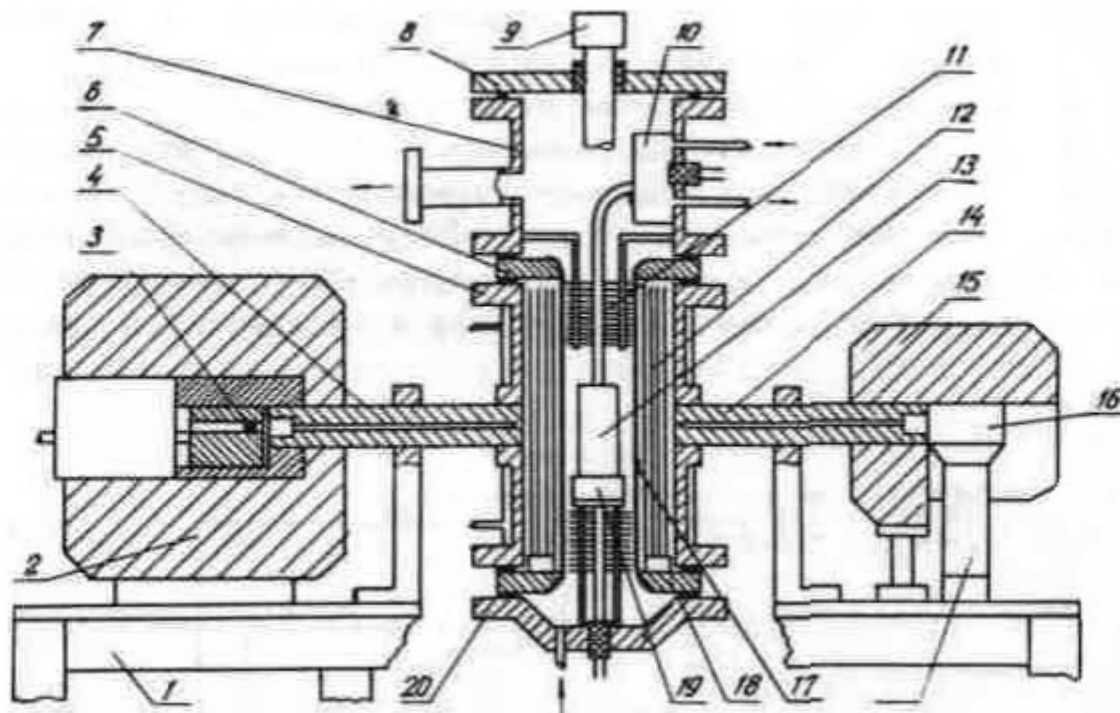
Принципиальная схема гамма-плотномера: 1 - опорный стол; 2, 15 - защитный контейнер; 3 - источник излучения; 4, 14 - коллиматоры; 5 - корпус печи; 6, 18 - токоподвод; 7 - форвакуумная камера; 8, 20 - крышки; 9 - загрузочное устройство; 10 - термостат холодных спаев; 11, 12 - экраны; 13 - измерительная ячейка с образцом; 16 - сцинтилляционный детектор излучения; 17 - нагреватель; 19 — опора.
